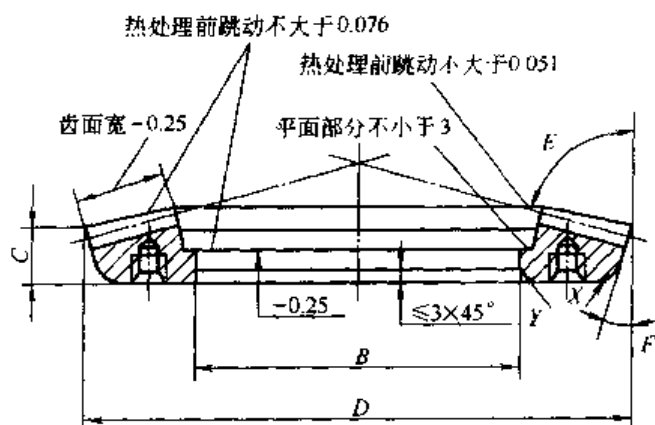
无凸缘环形齿轮的轮坯公差
